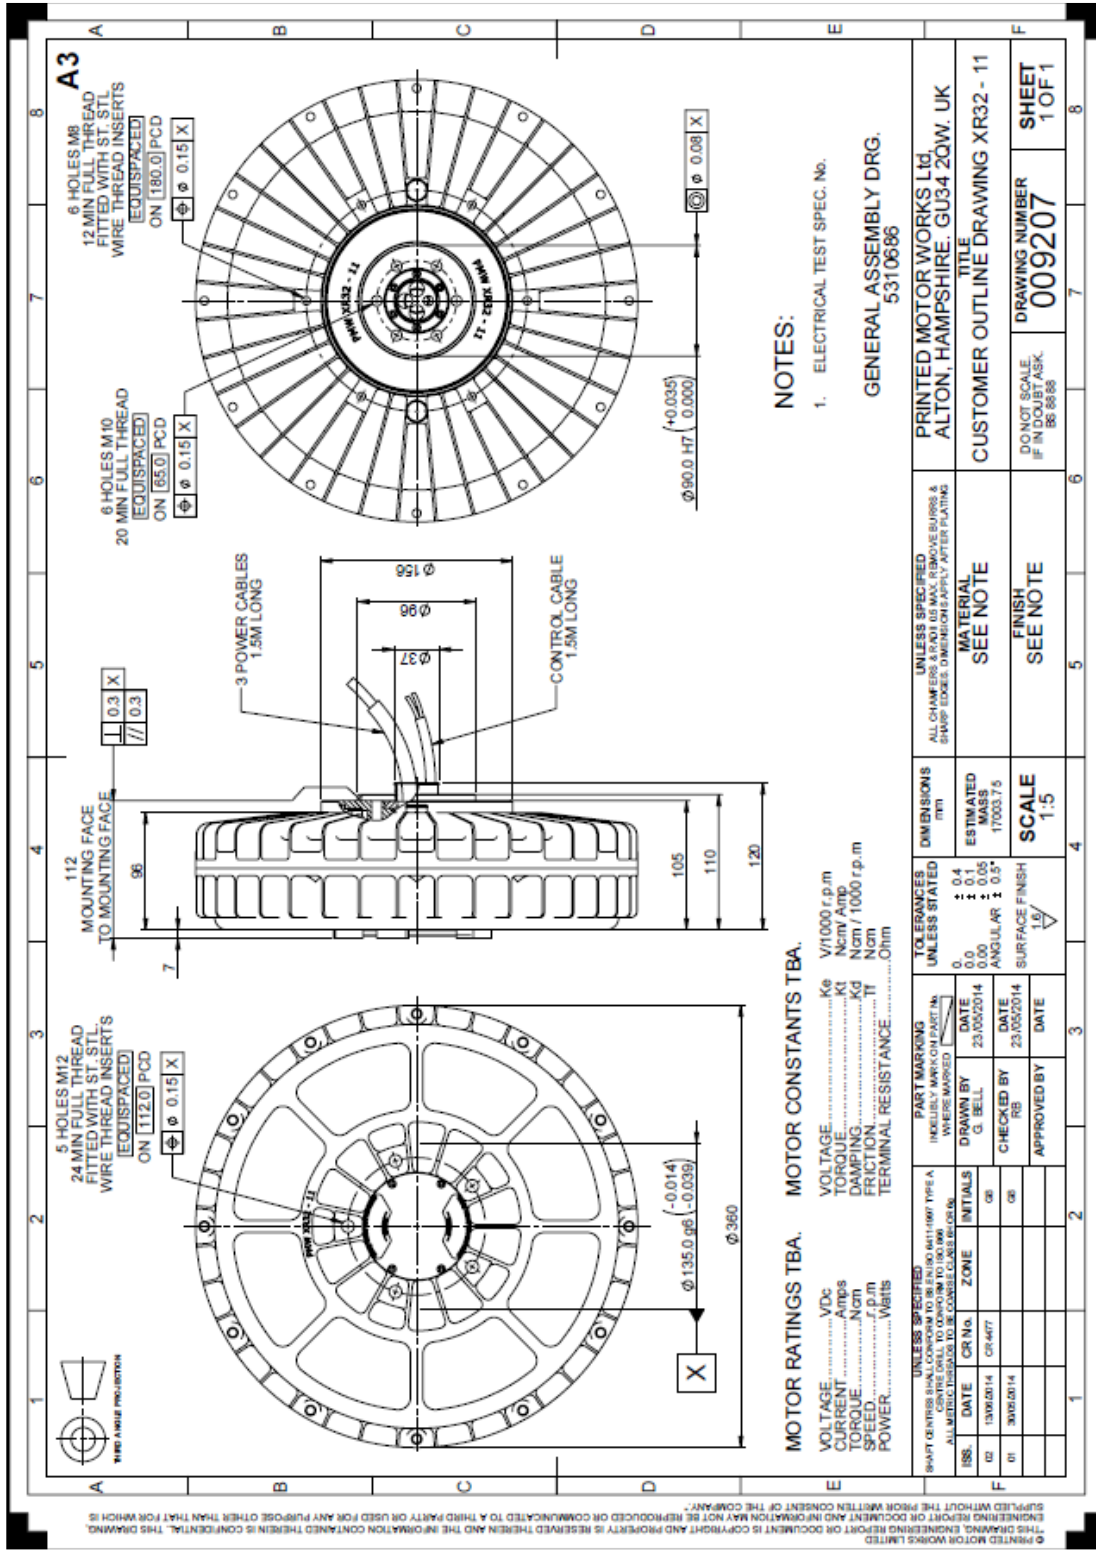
Plànol Printed Motor Works XR32-11-009207 (Printed Motor Works, s.f.)
